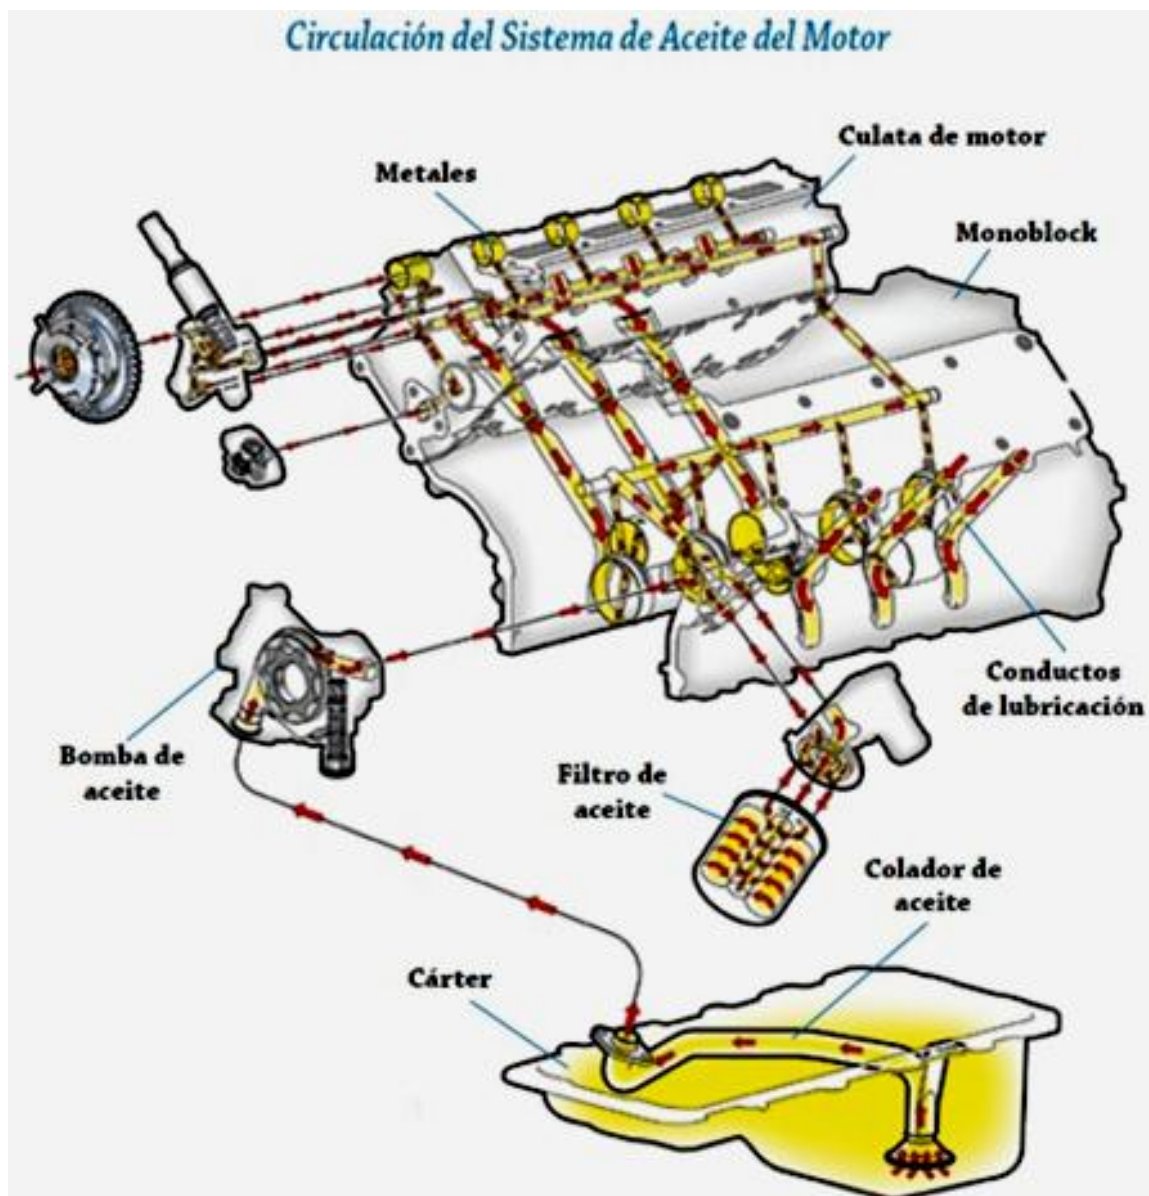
Lubricación en un motor de combustión interna del ciclo Otto. (Referencia 9).
